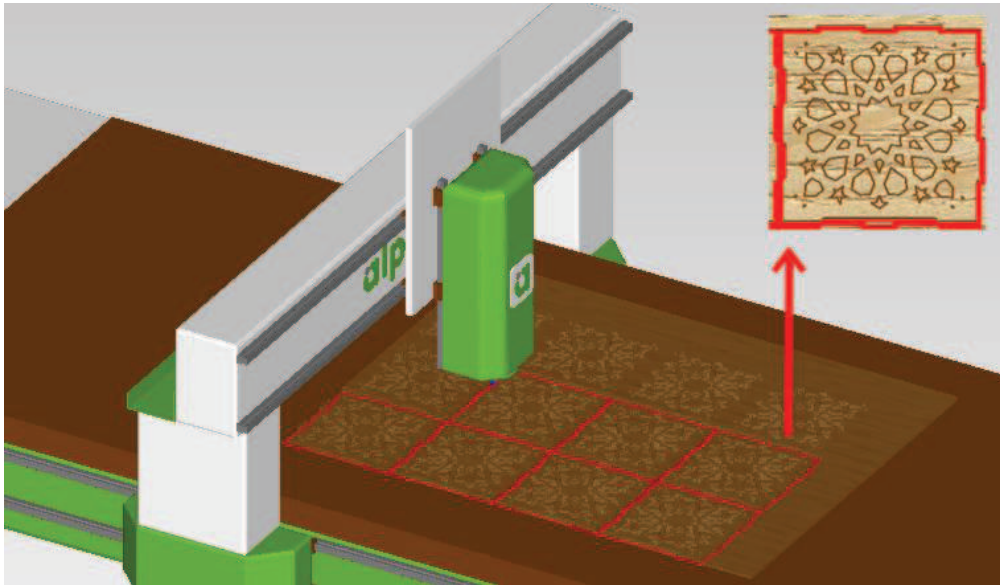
Peça que necessita de rotação para ser encaixada
